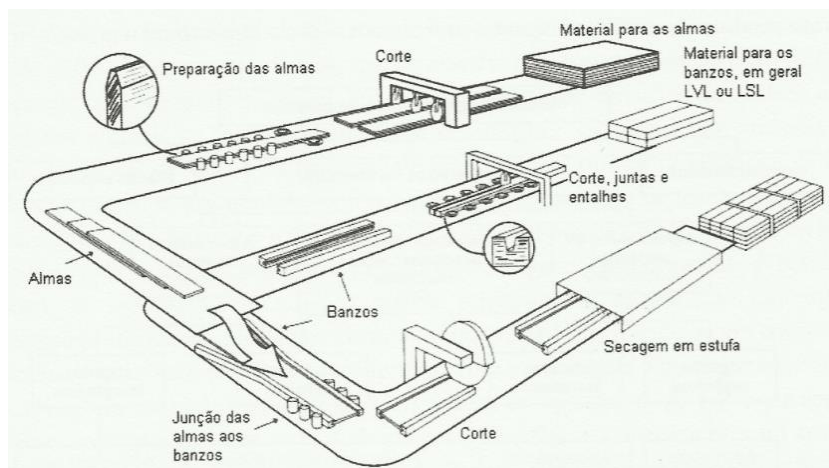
Fases de produção da Vigas I (Cachim, P., 2007)
